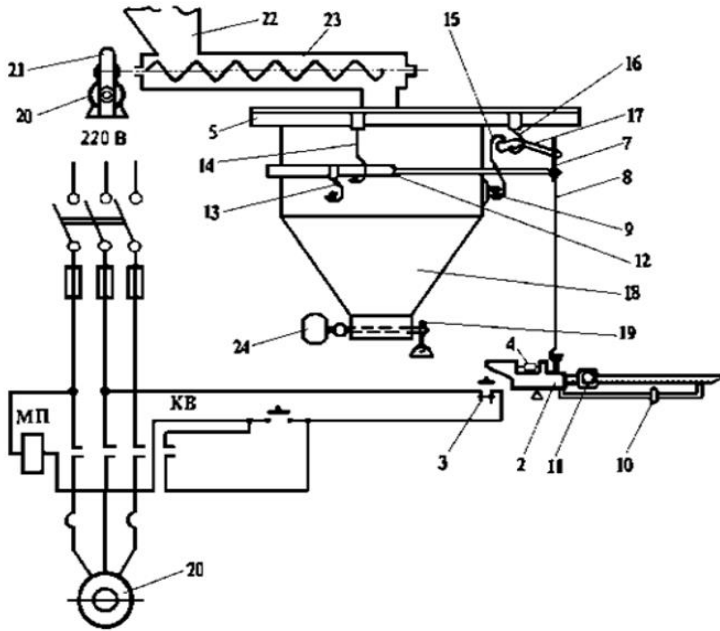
Дозатор борошна ваговий МД-100: 1 – кожух; 2 – вагове коромисло; 3 – ргутний переривник; 4 – балансувальна гиря; 5 – рама; 6 – підвіска; 7 – подвійна сержка; 8 – тяга; 9 – призми; 10 – гиря додаткової шкали коригування ваги; 11 – пересувана гиря; 12 – подвійний важіль; 13, 14, 15, 16 – сержки; 17 – малий важіль; 18 – бункер; 19 – заслінка; 20 – електродвигун; 21 – редуктор; 22 – силос; 23 – живильний шнек; 24 – виконавчий механізм відкриття заслінки.
